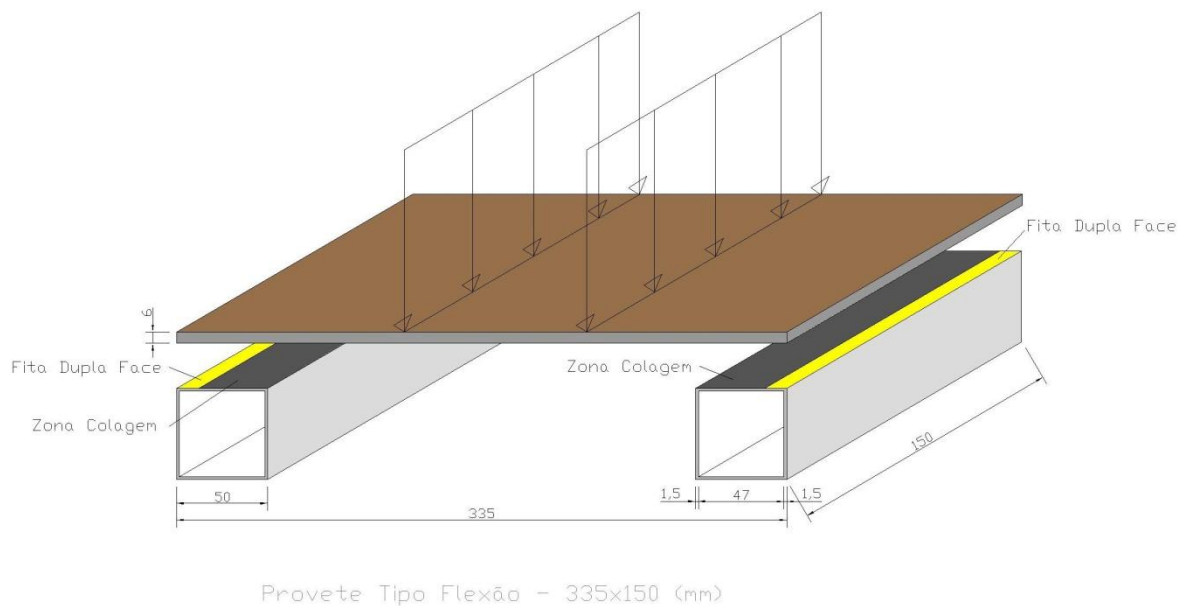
Esquema exemplificativo de um provete a ensaiar à flexão (dimensões em mm)
